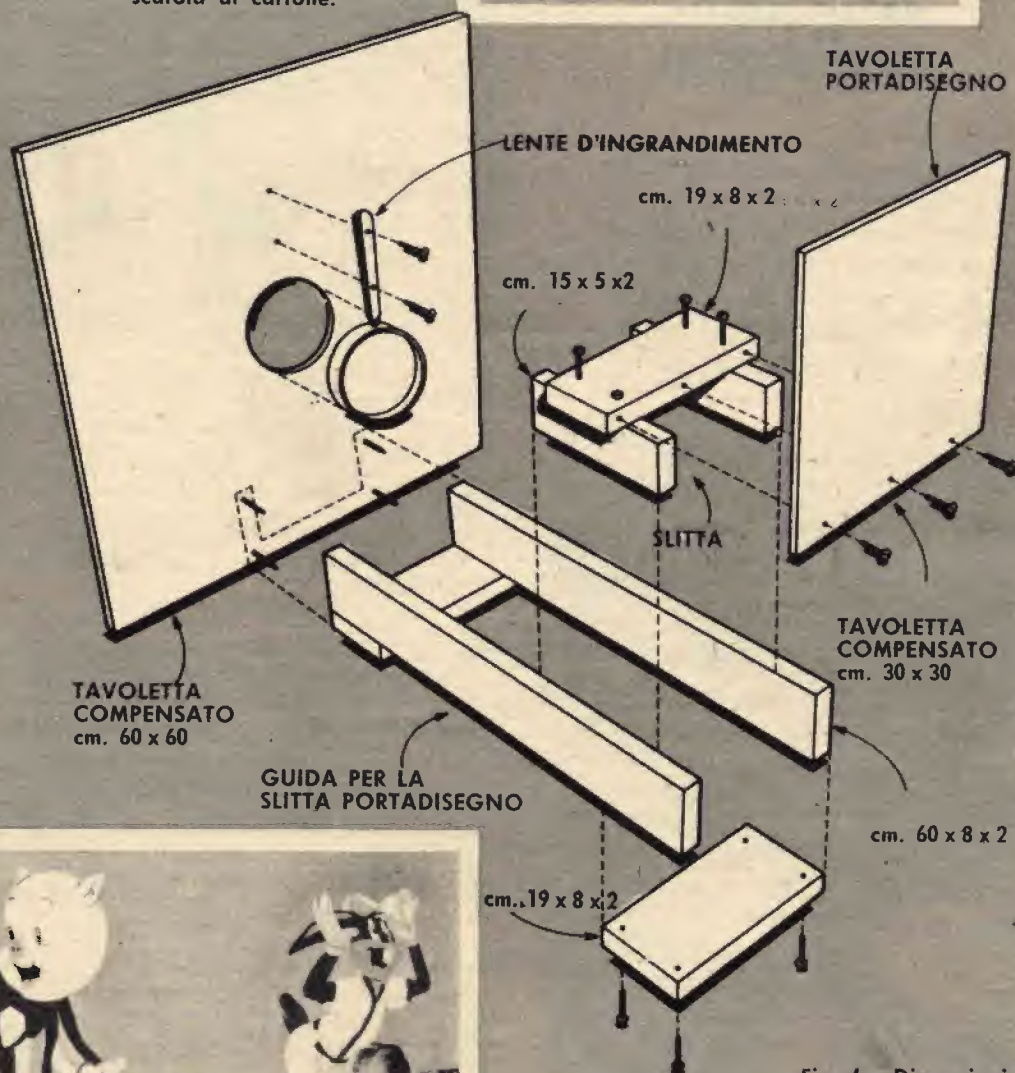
Dimensioni delle varie parti che compongono il proiettore.
